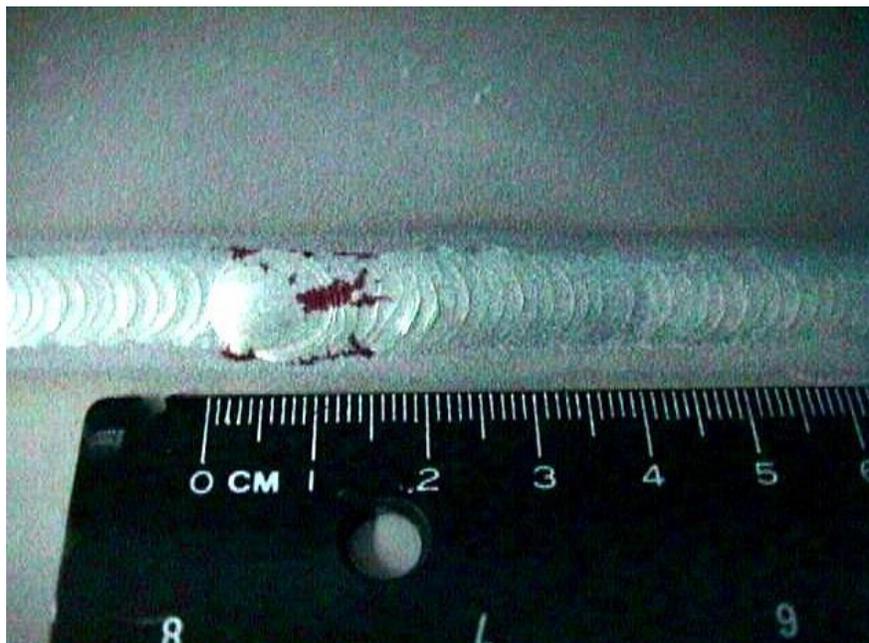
Indicaciones en la técnica de líquidos penetrantes
